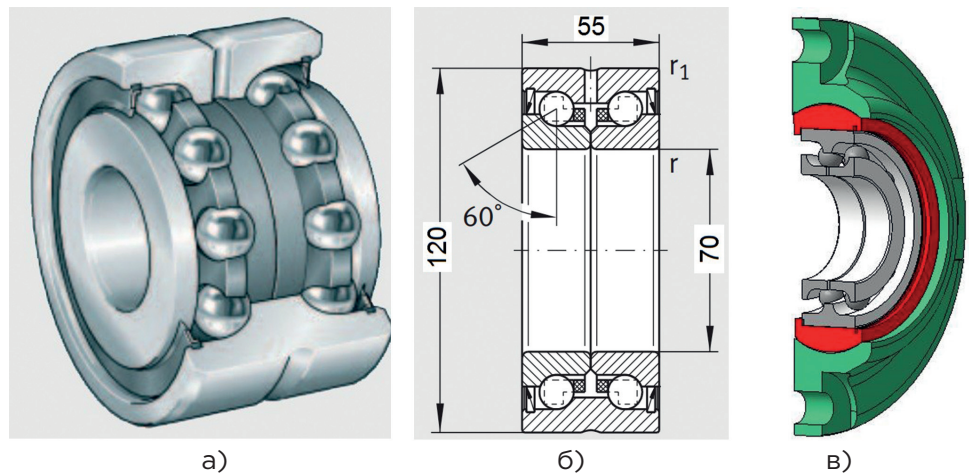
Підшипник ZKLN70120-2Z фірми «INA» та схема запропонованої конструкції опори
